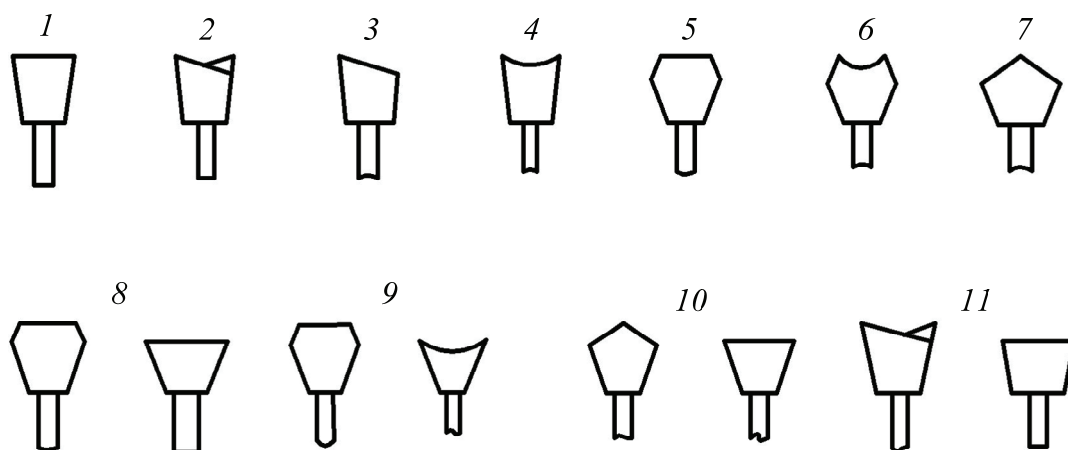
Формы зубьев пил с твердосплавными пластинами:
